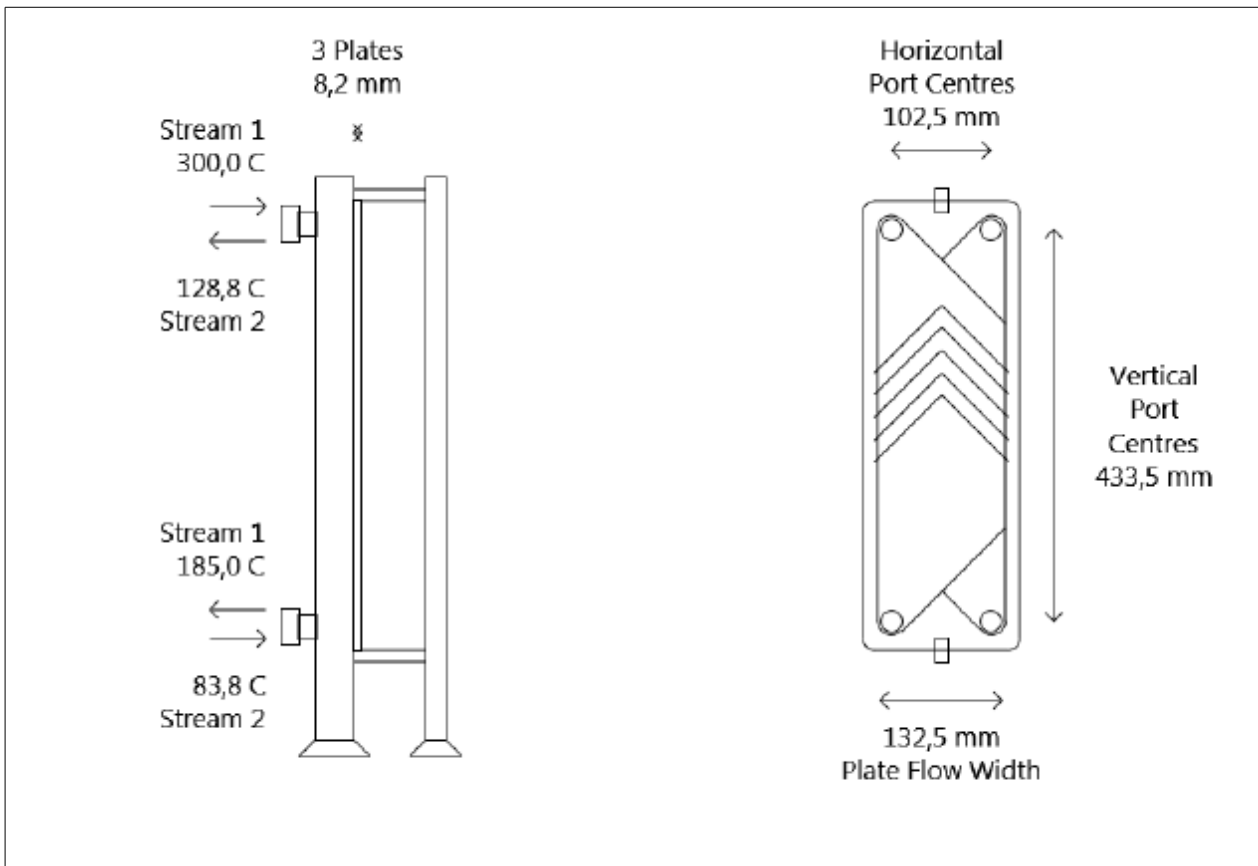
Corte transversal para observar las dimensiones de una placa (derecha) y alzado del intercambiador de placas (izquierda).
